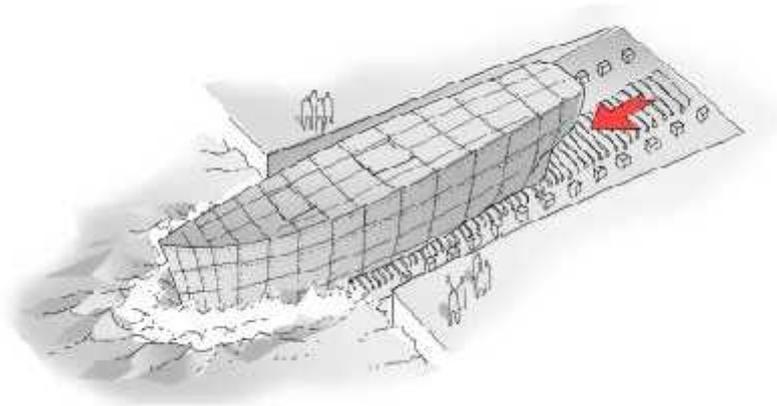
Construcción de un barco por el sistema de remaches.
